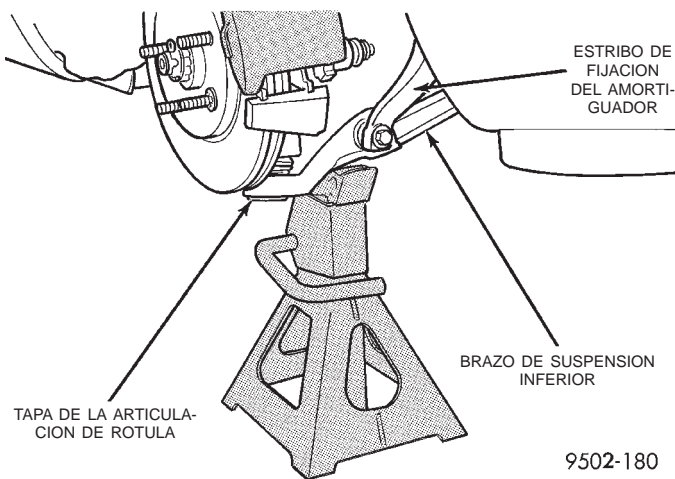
Estribo de fijación instalado correctamente en el amortiguador
